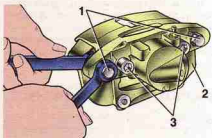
Отворачивание болта крепления цилиндра: 1 – болты крепления цилиндра; 2 – цилиндр; 3 – болты, стягивающие цилиндр с суппортом
